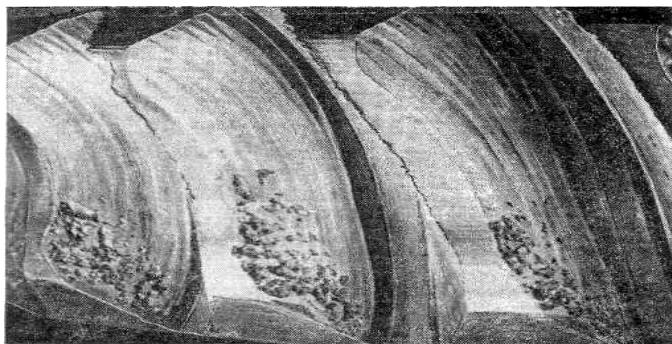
Выкрашивание рабочих поверхностей зубьев червячного колеса
